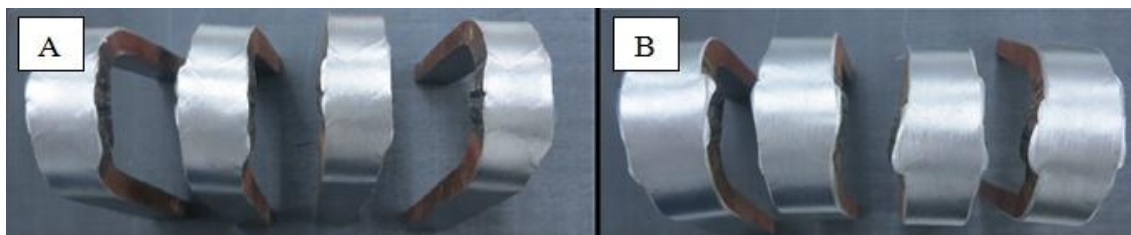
Ensaio de dobragem - Superfície de dobragem dos provetes soldados com A) FLUXOFIL 19 HD e B) FABSHIELD XLR-8
